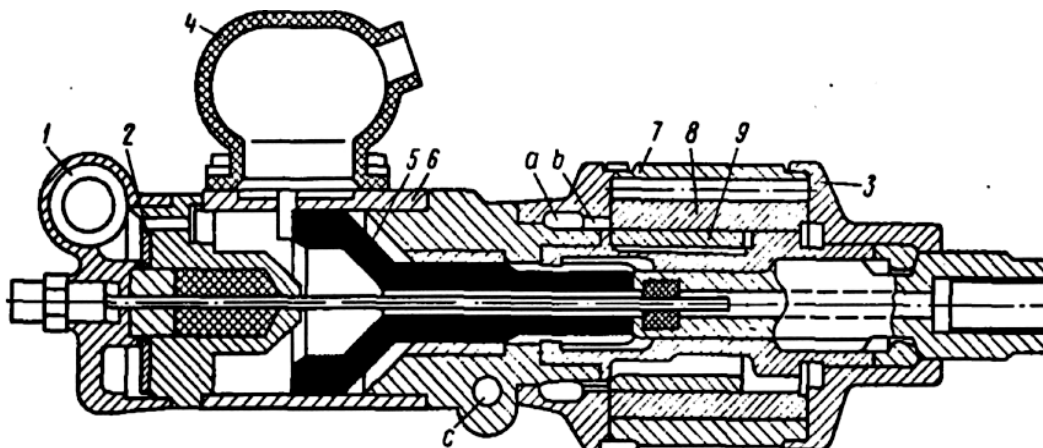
Вращательно-ударный пневматический перфоратор
